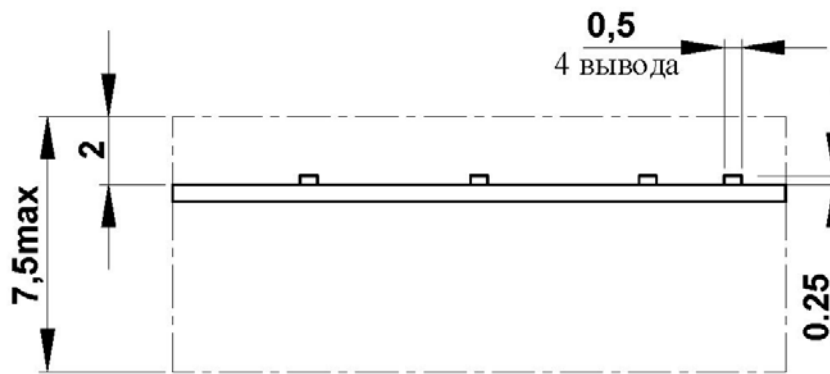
Габаритный чертеж модулей в конструктивном исполнении «Н»
